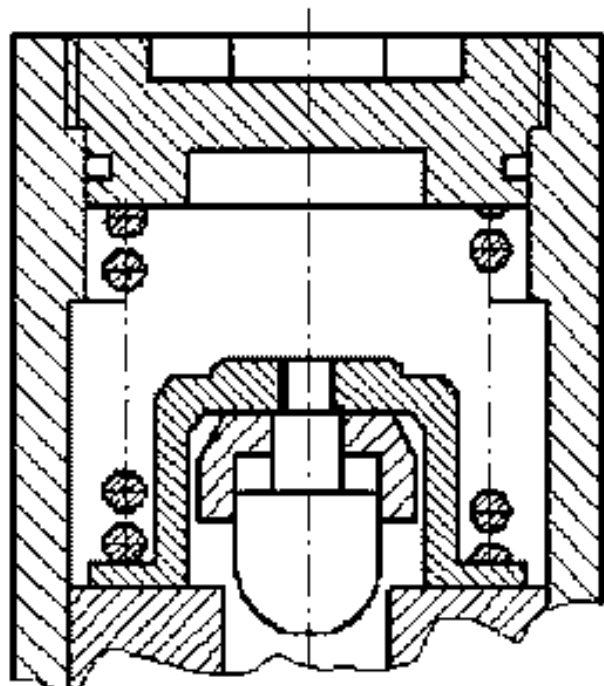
Образец изображения пружины на сборочном чертеже.
